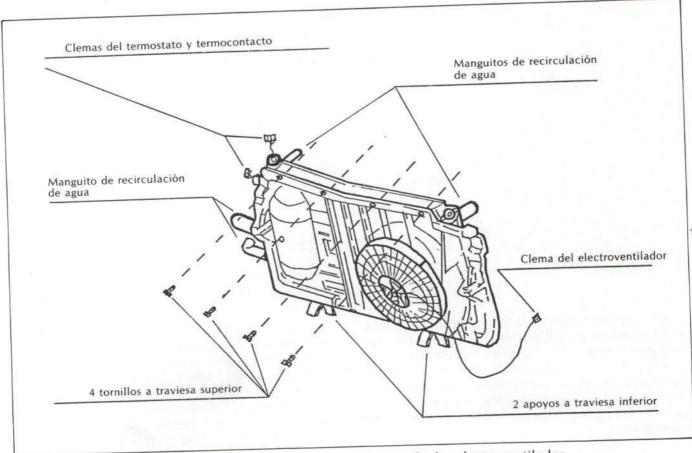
Montaje del conjunto carcasa-radiador-electroventilador.
